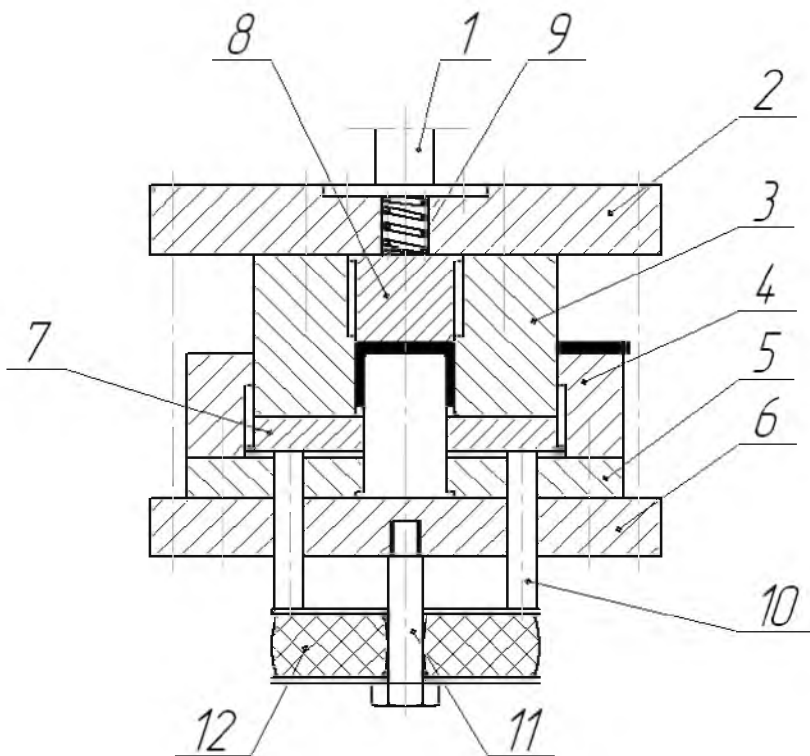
Схема штампа совмещённого действия для отрезки и гибки
